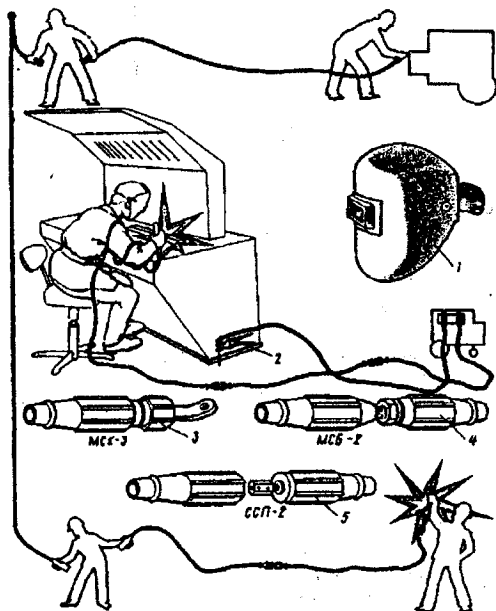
Пост для ручного зварювання покритими електродами
